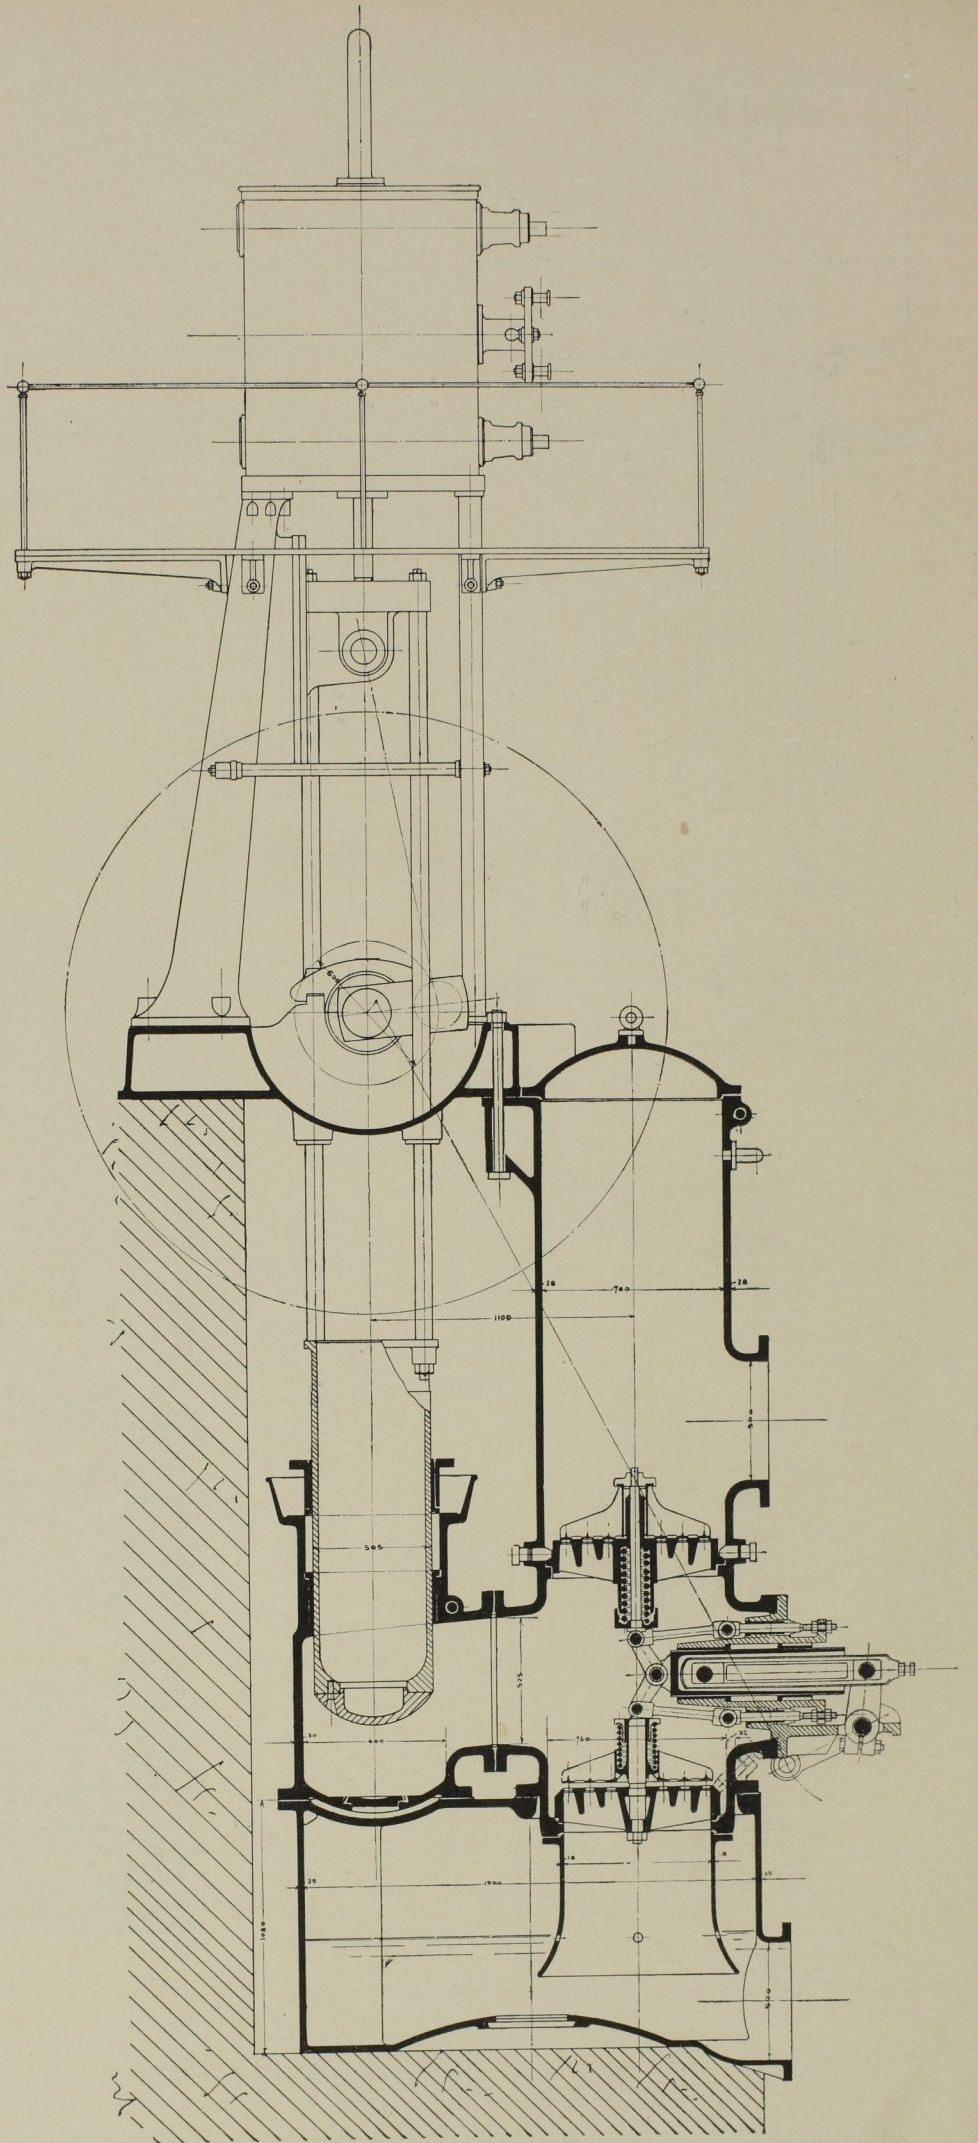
Seitenansicht und Schnitt der Pumpmaschine. Masst. 1:30.
